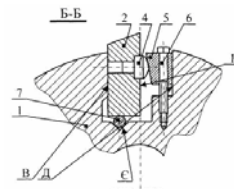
Узел крепления режущего элемента червячной фрезы для обработки крупногабаритных зубчатых колес
